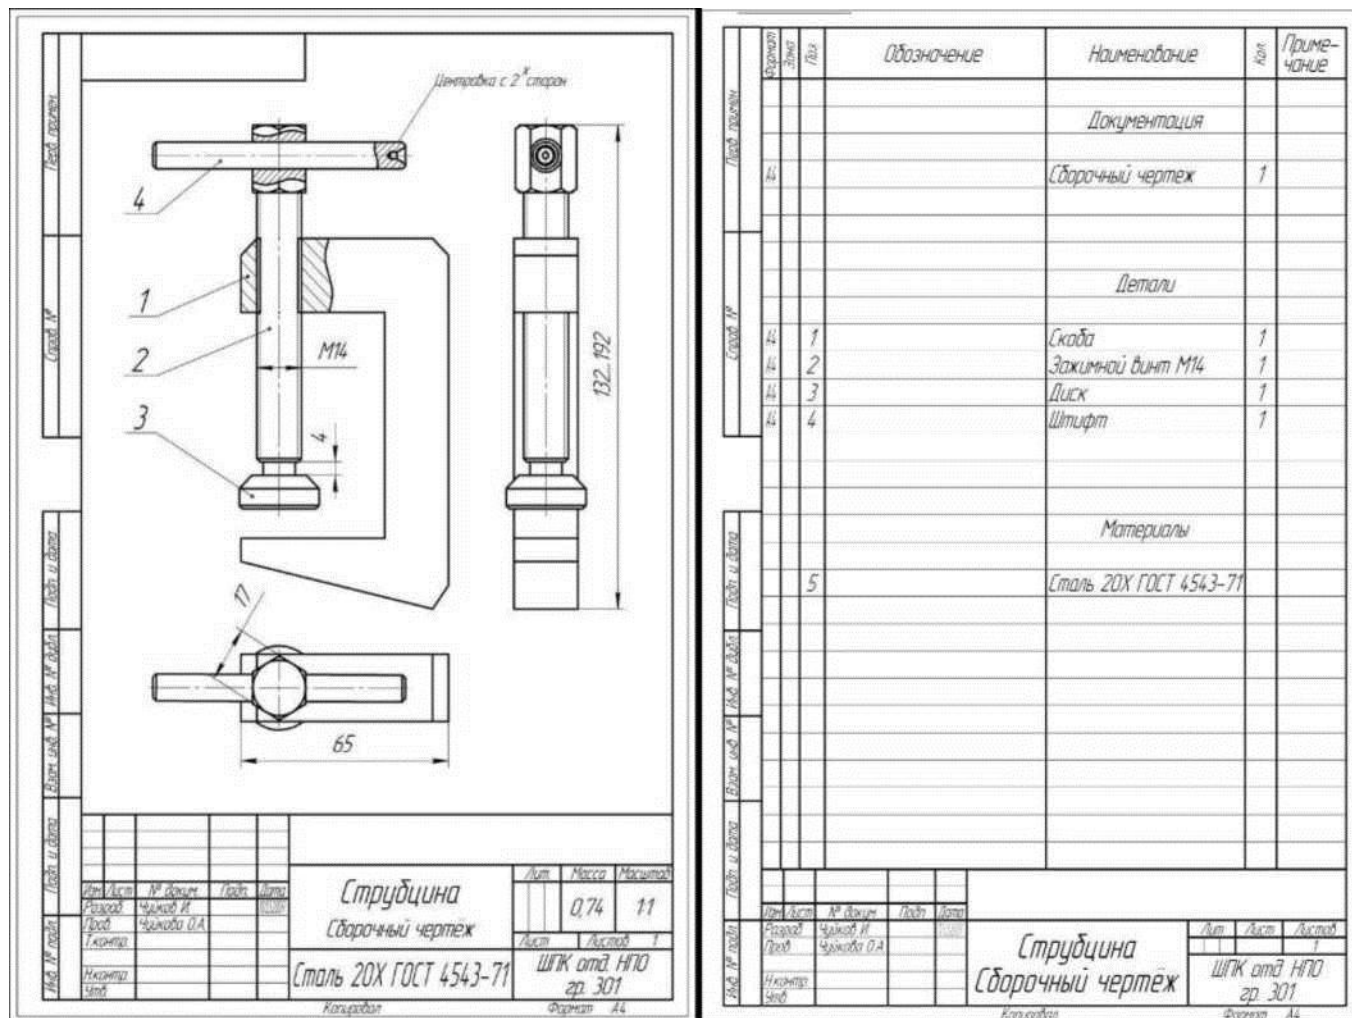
Сборочный чертёж струбцины со спецификацией
